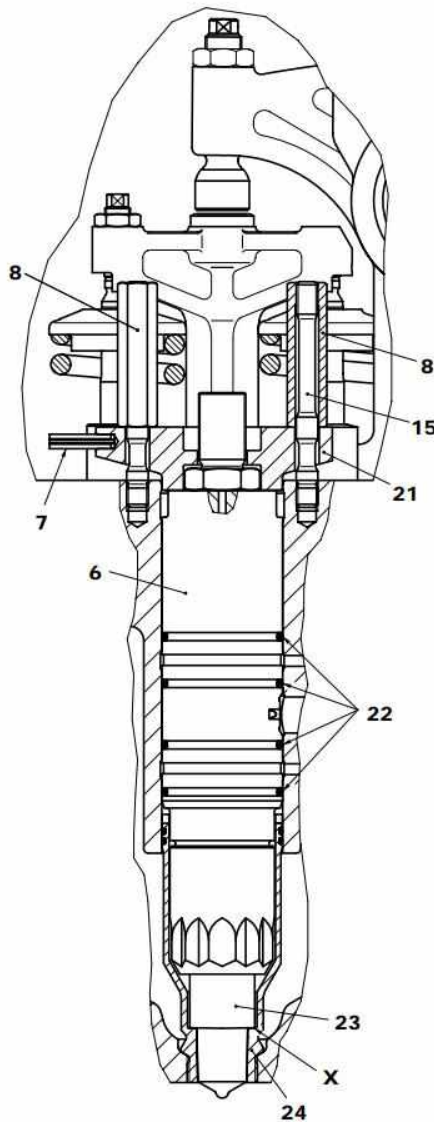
Паливна форсунка двигуна типу MaK M25C: 8 – гайка; 15 – шпилька; 22 – ущільнювальні кільця; 23 – сопло; 24 – втулка
